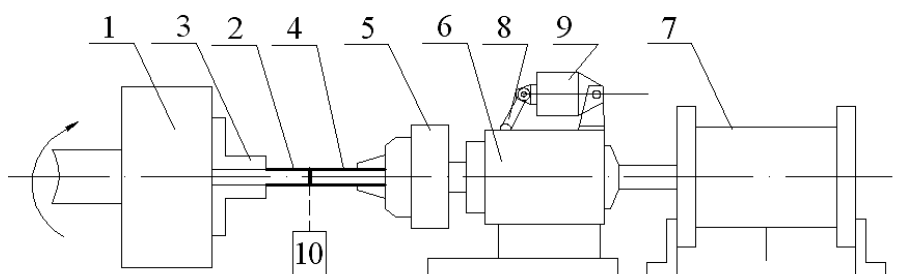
Схема установки для получения образцов для исследования стойкости наплавленного металла против схватывания:
